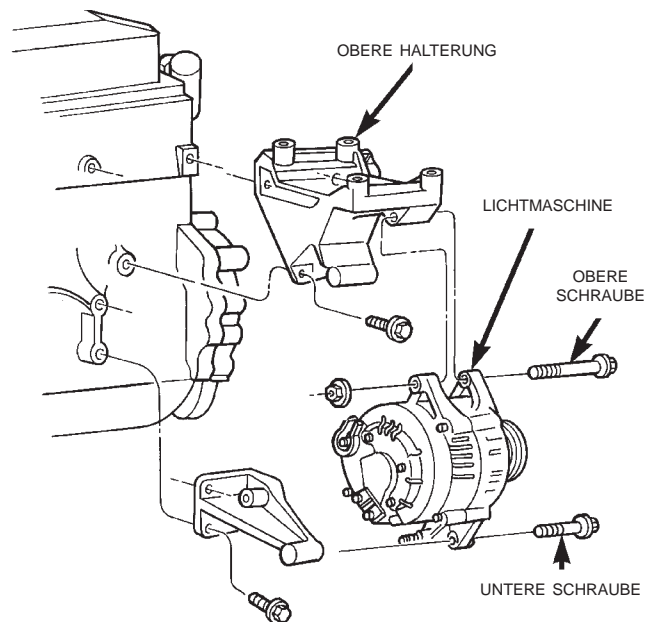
Lichtmaschine aus- und einbauen—2.5L-Motor
